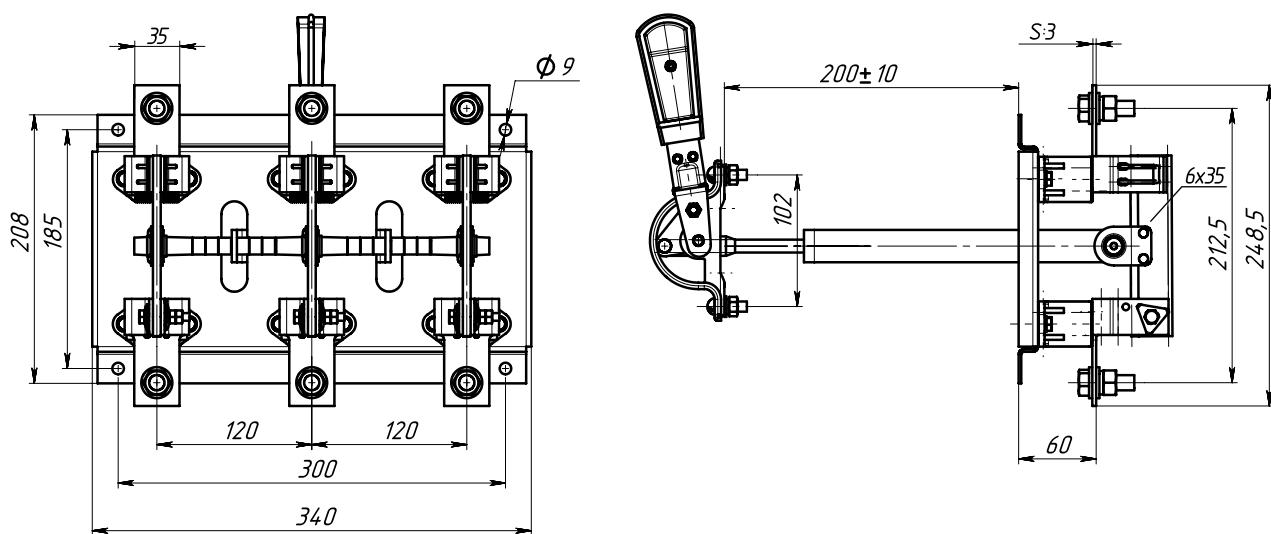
Разъединитель серии Р с центральным приводом, РЦ-6
